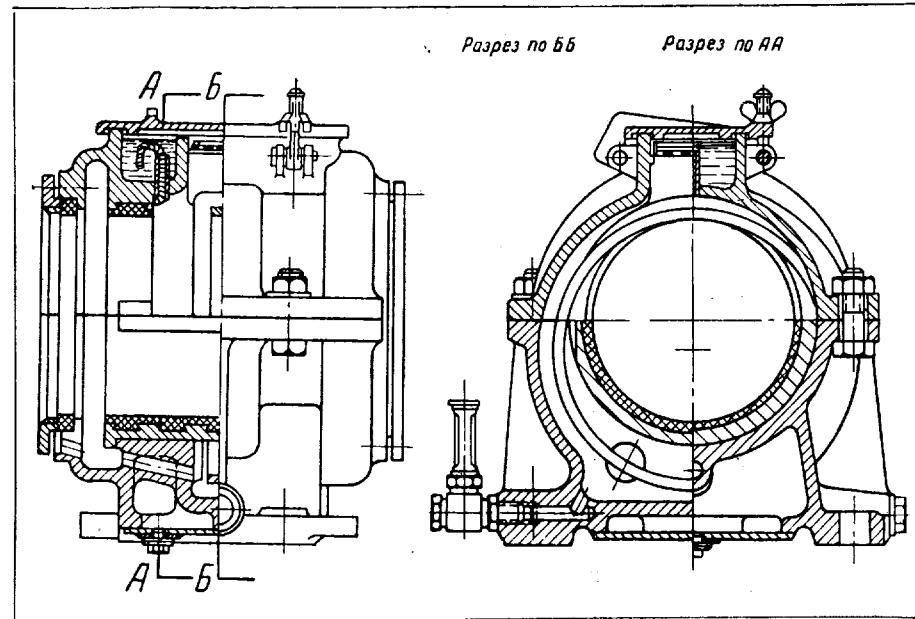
Опорный подшипник с кольцевой смазкой (тип II)
